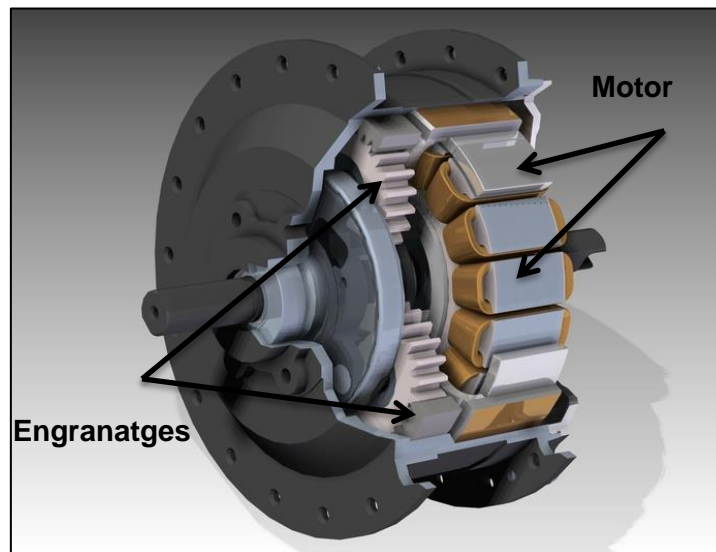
Motor amb engranatges (MORCHIN, 2006)
